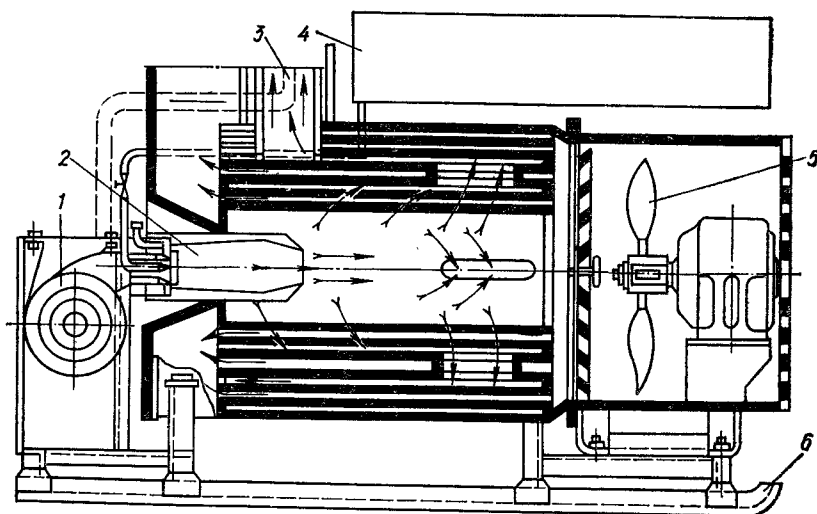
Универсальный строительный воздухонагреватель УСВ-200:
